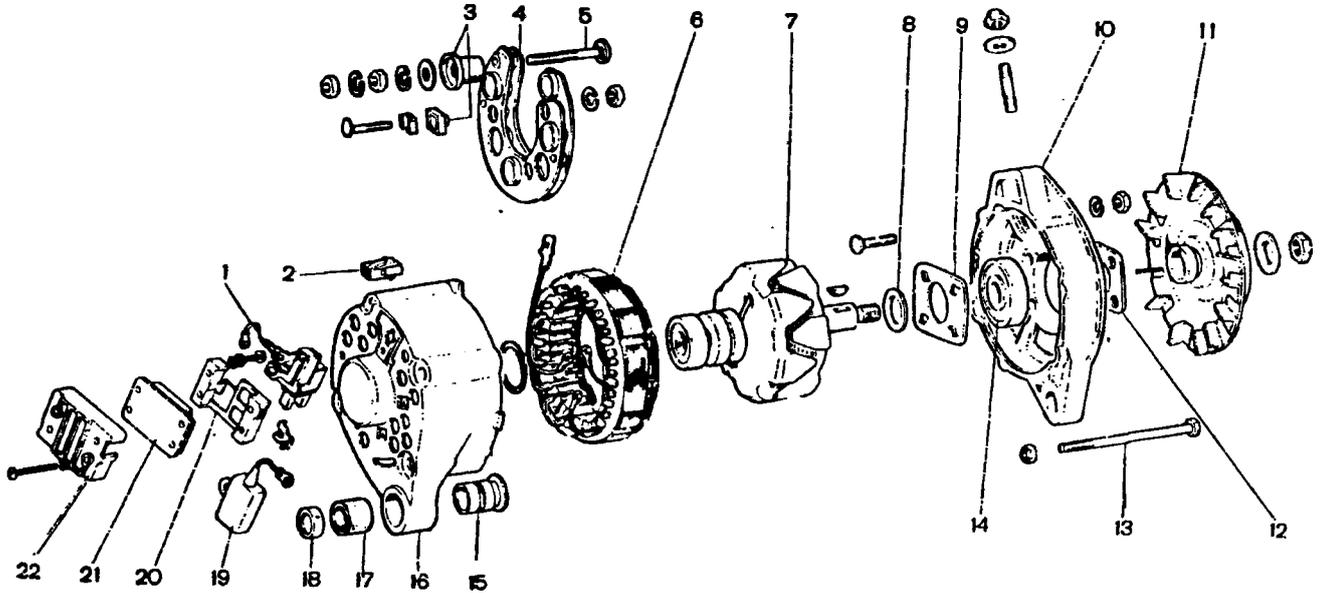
Детали генератора Г-222: 1 - щеткодержатель; 2 - колодка щетки нулевого провода; 3 - изолирующие втулки контактного болта; 4 - выпрямительный блок; 5 - контактный болт; 6 - статор; 7 - ротор; 8 - шайба; 9 - внутренняя шайба крепления подшипника; 10 - крышка со стороны привода; 11 - шкив; 12 - наружная шайба крепления подшипника; 13 - стяжной болт; 14 - подшипник ротора; 15 - поджимная втулка; 16 - крышка со стороны контактных колец; 17 - буферная втулка; 18 - втулка; 19 - конденсатор; 20 - основание; 21 - регулятор напряжения; 22 - кожух
